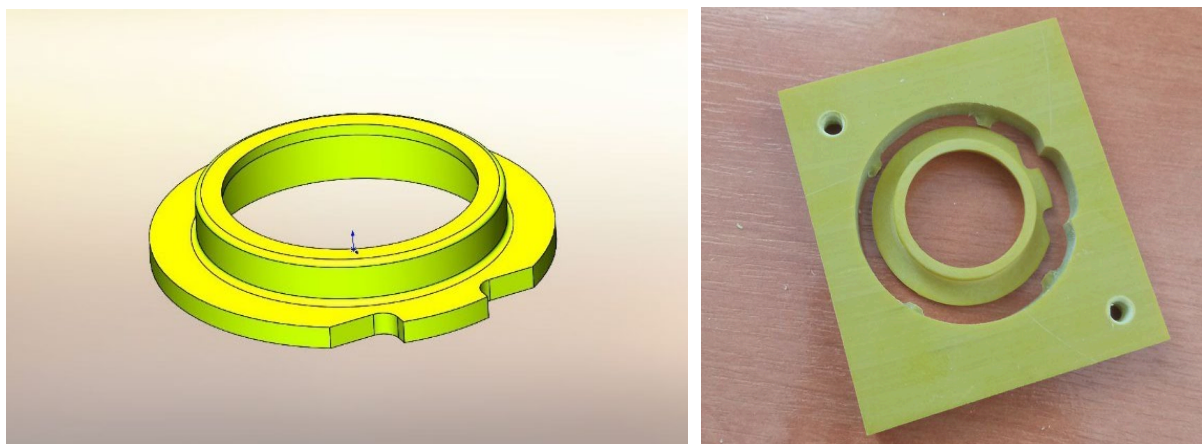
Тривимірна модель та деталь Проставка виготовлена на станку з ЧПК.
